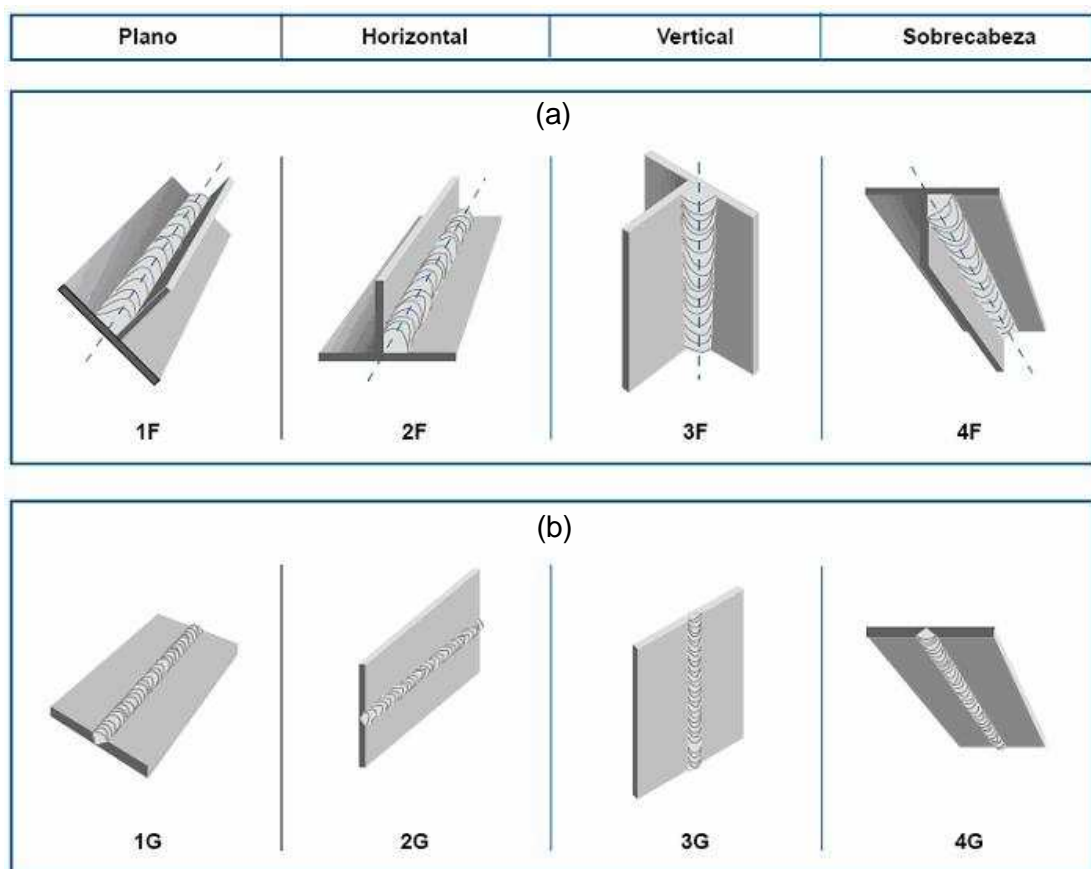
Posiciones de soldadura: a) Uniones de filete, b) Uniones biseladas
